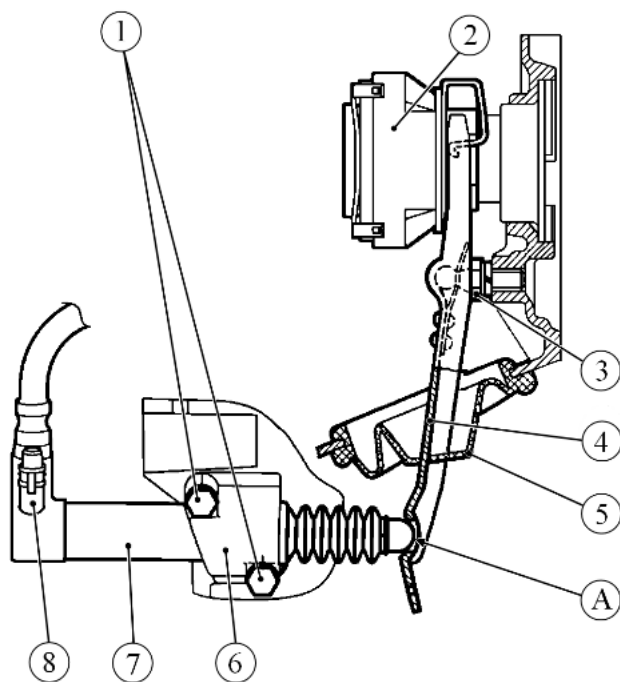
Рабочий цилиндр и вилка выключения сцепления:
